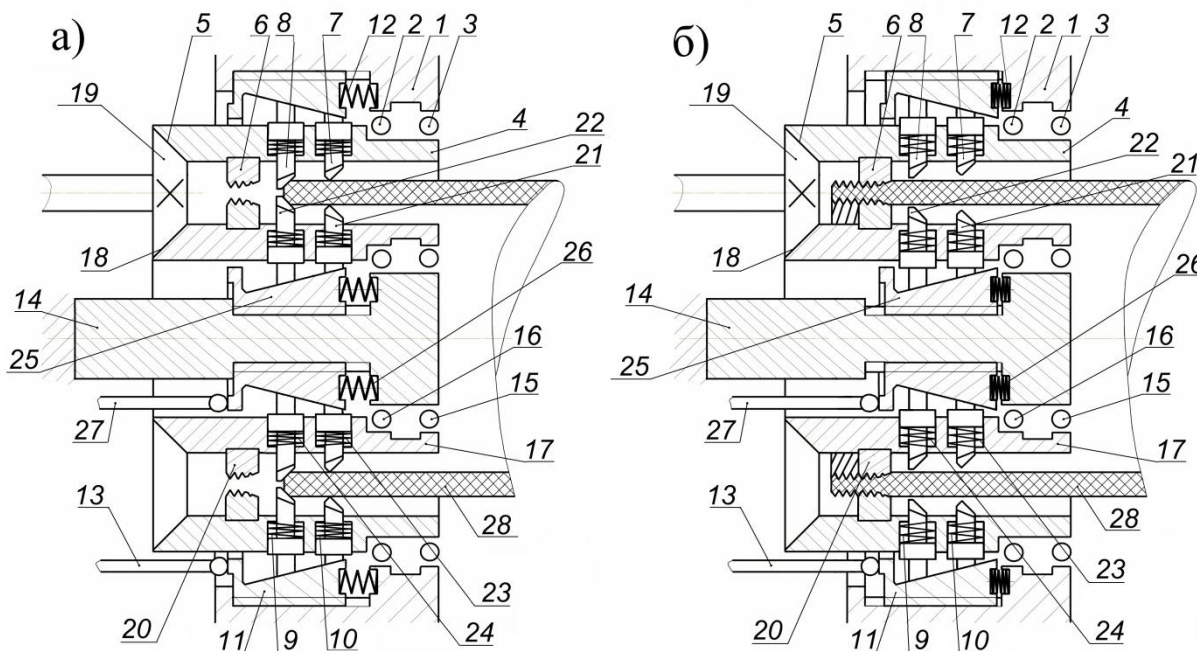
Устройство для механической обработки концов труб из ПКМ:
